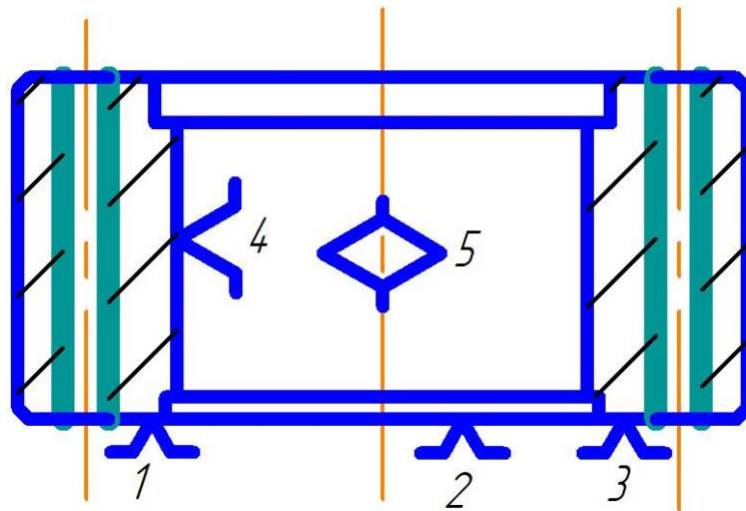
Принципиальная схема зажима заготовки в приспособлении с указанием мест приложения силы зажима.
